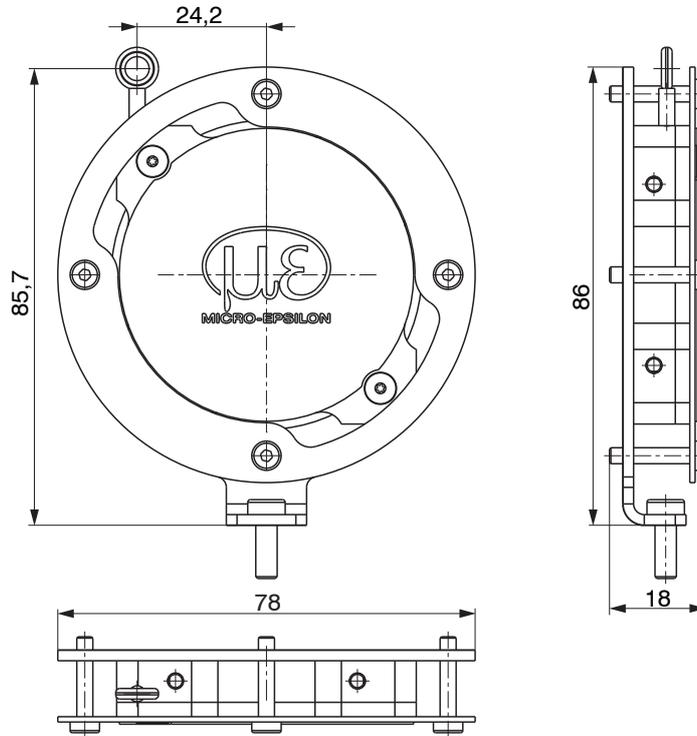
Maßzeichnung WDS-MB56 Montagewinkelset - Seitenansicht, Abmessungen in mm
